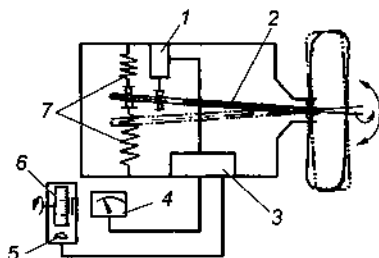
Балансировочный станок К-121: 1 — индикаторный датчик; 2 — вал; 3 — электронный блок; 4 — прибор; 5 — стробоскопическая лампа; 6 — градуированный диск; 7 — резонирующий механизм
